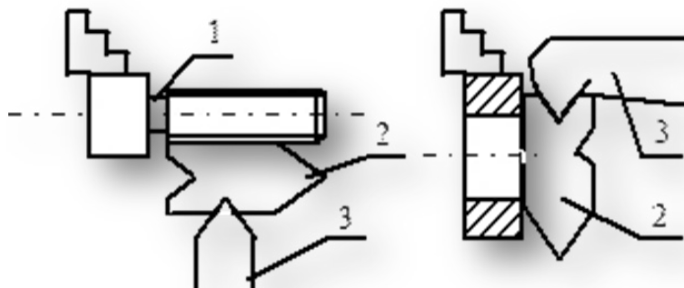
Встановлення різьбового різця за шаблоном: 1 – заготовка; 2 – шаблон; 3 – різець
